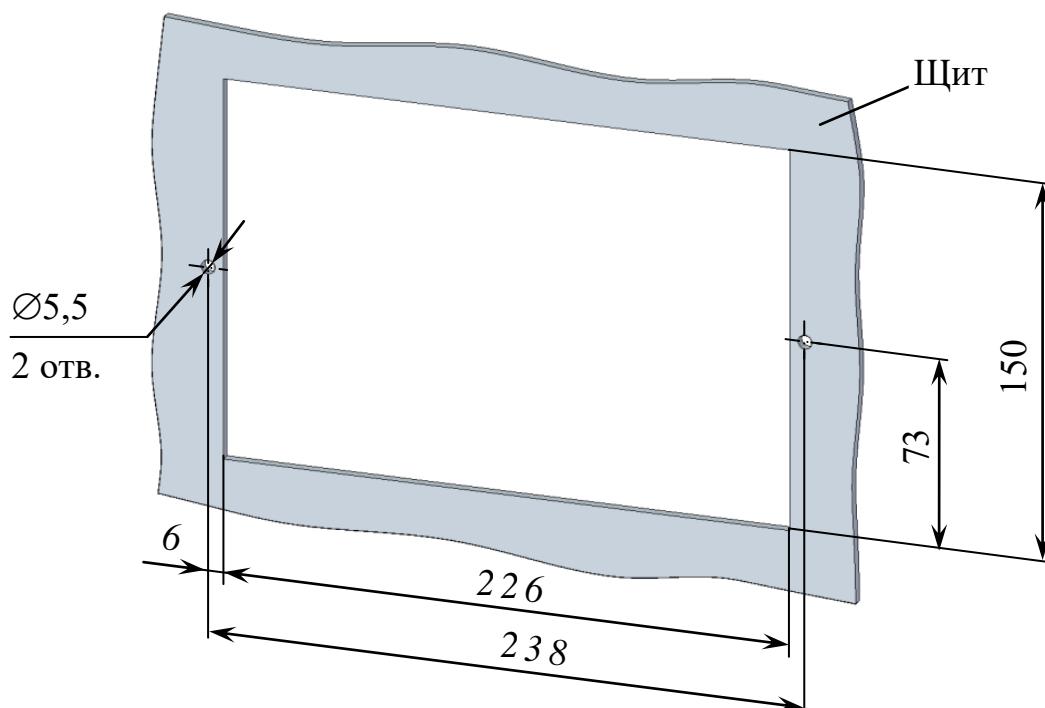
Расположение и размер отверстий для крепления блока преобразовательного щитового исполнения в щите
